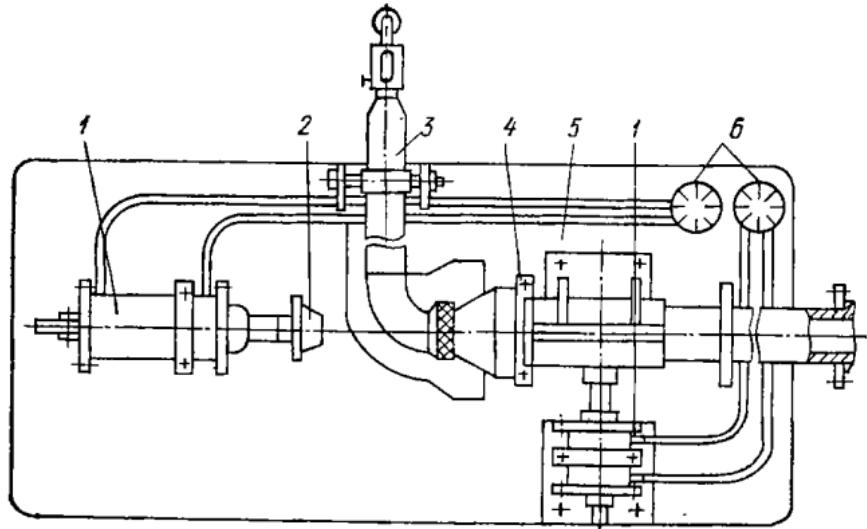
Установка для отбортовки фторопластовых труб с нагревом:
